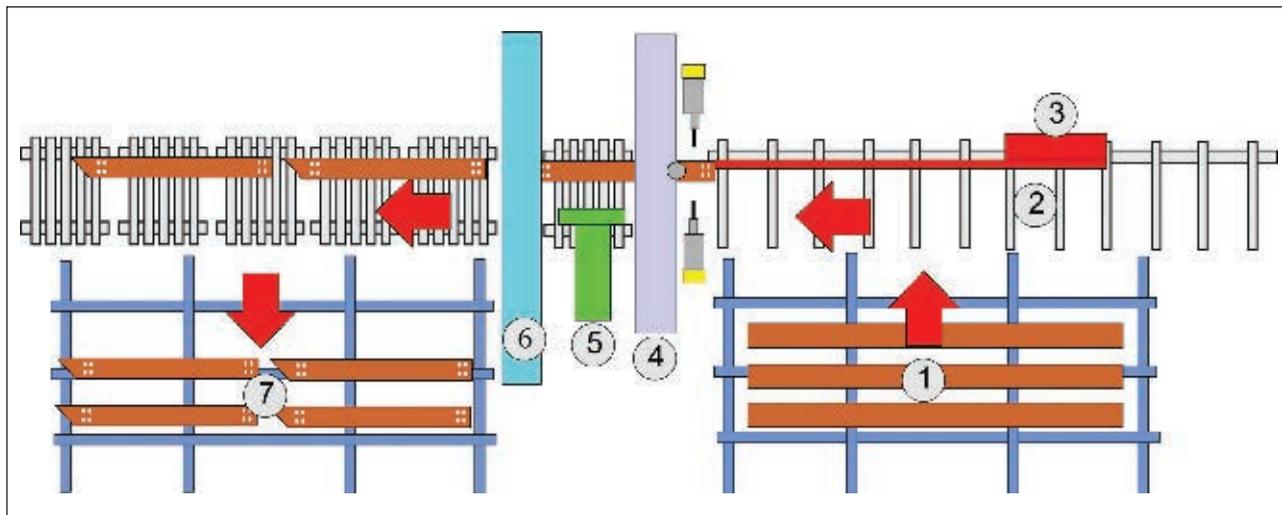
Линия сверловки, маркировки и мерной порезки профильного проката: 1 — загрузочный конвейер; 2 — транспортная система; 3 — подающее устройство; 4 — установка для сверления в трех плоскостях; 5 — установка для маркировки; 6 — установка для мерной порезки; 7 — принимающий конвейер
